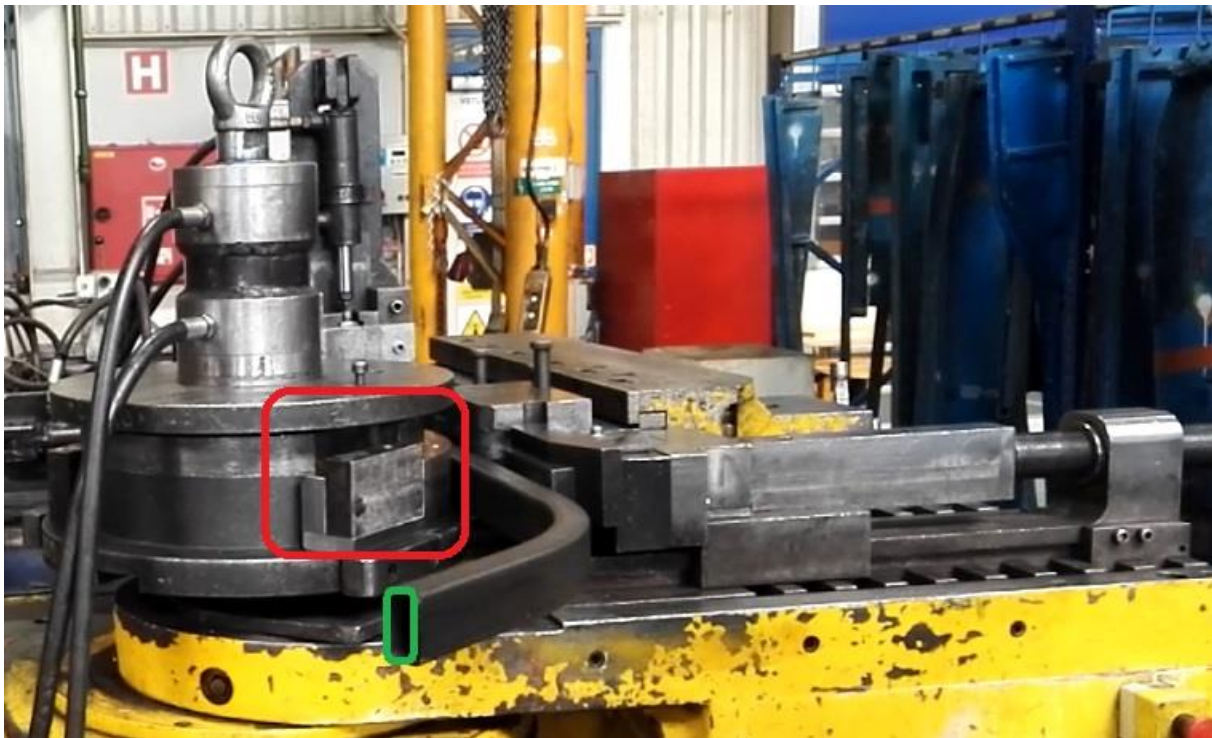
Kompletně svařený přípravek spolu s drážkovanou deskou a podložkou
